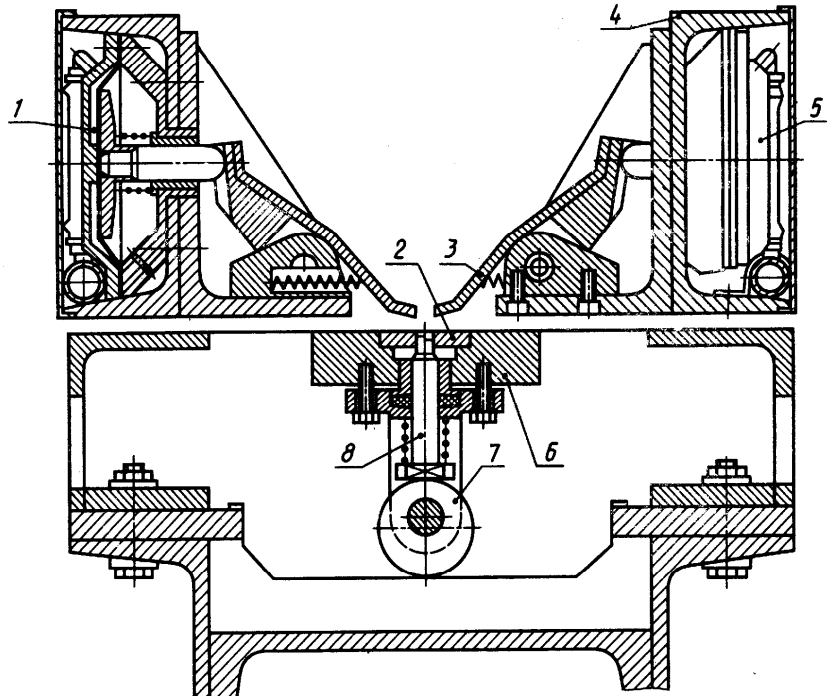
Приспособление пневмодиафрагменного типа для автоматической сварки прямолинейным швом
